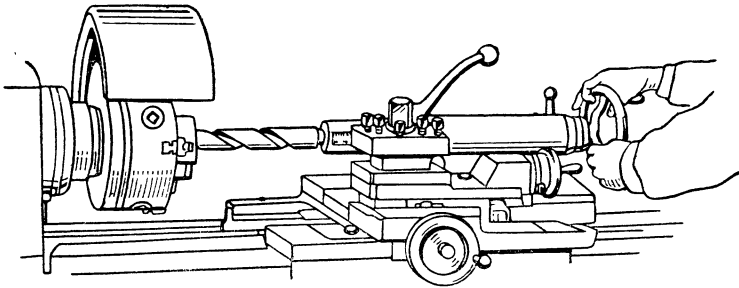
Патрон для закрепления сверла с цилиндрическим хвостовиком.
